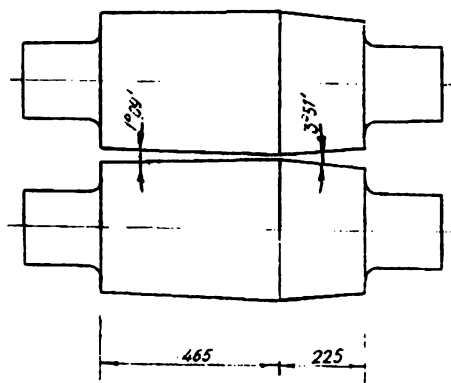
Двухконусные валки чистовой клетки 8-350
